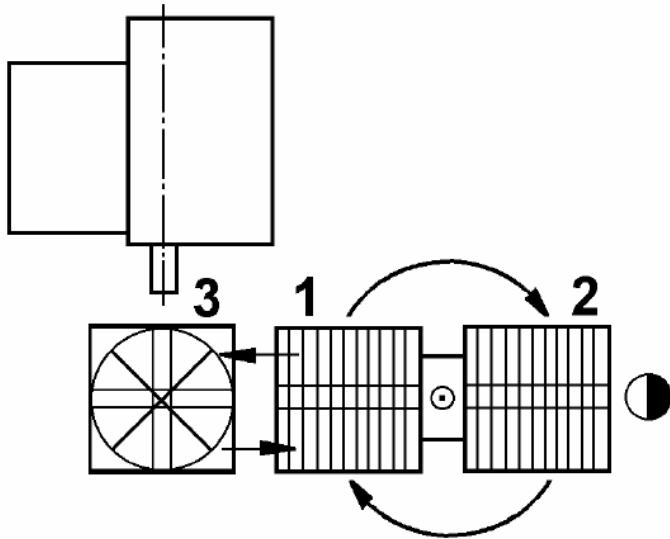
Řetězové skladovací zásobníky[ŠMT Plzeň 2010]
